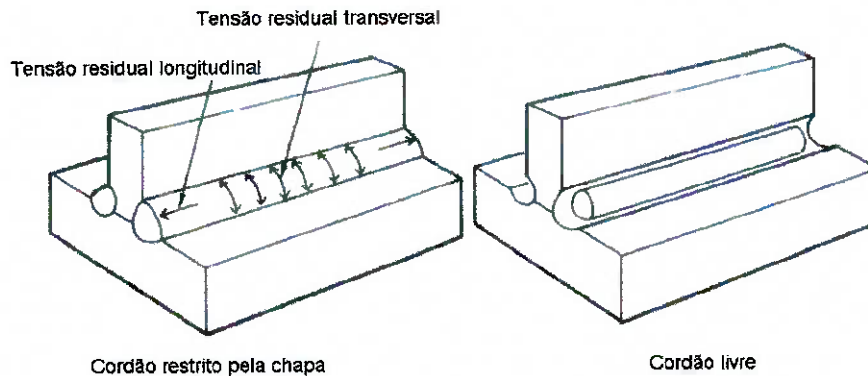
Comportamento de um cordão de solda em uma junta soldada [13, adaptado]
